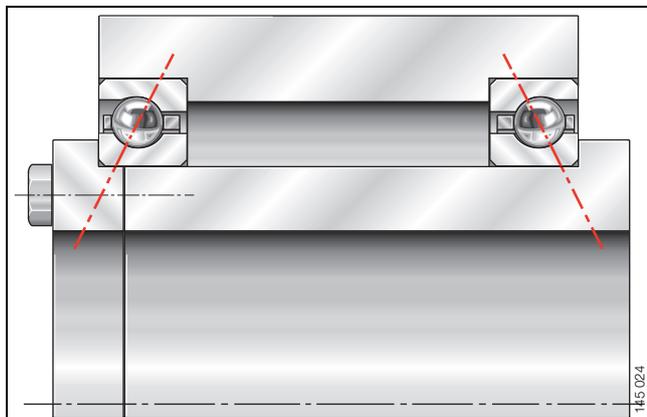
· Kombinierte Schrägkugellager, O-Anordnung, Gehäuse mit zweiseitigem Bund
